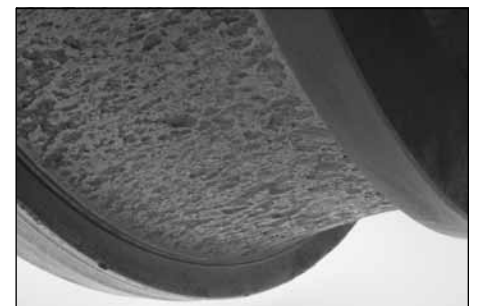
La sobrecarga en este rodamiento de rodillos cilíndricos ocasionó una fractura en la superficie de los rodillos.
